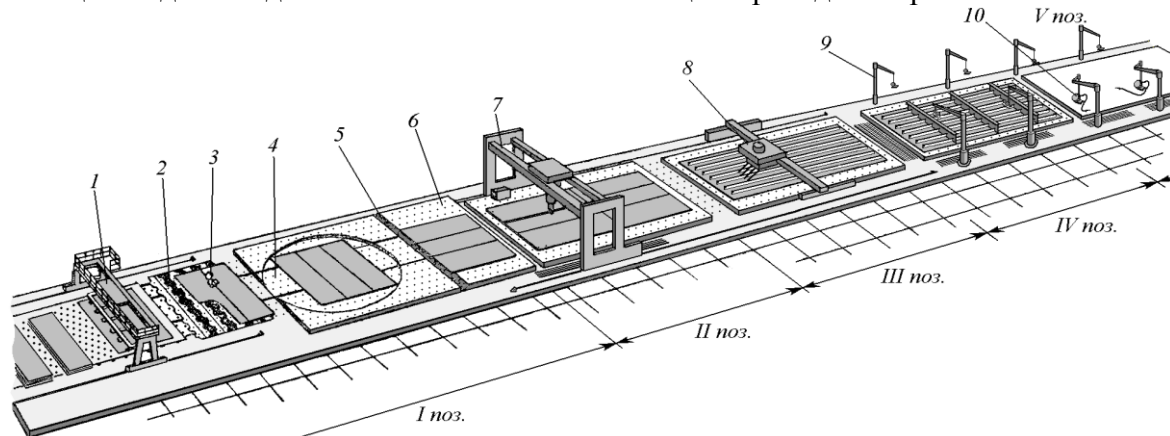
Общий вид механизированной поточной линии для изготовления крупногабаритных плоскостных секций:
